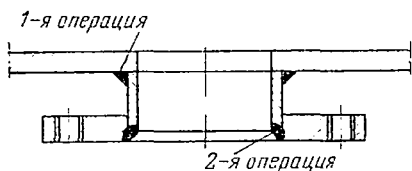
Порядок приварки коротких патрубков с широкими фланцами.
